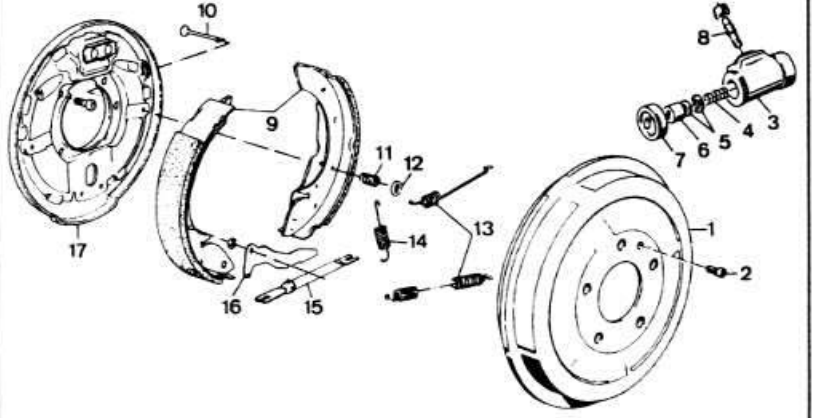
Детали барабанного тормозного механизма заднего колеса:
